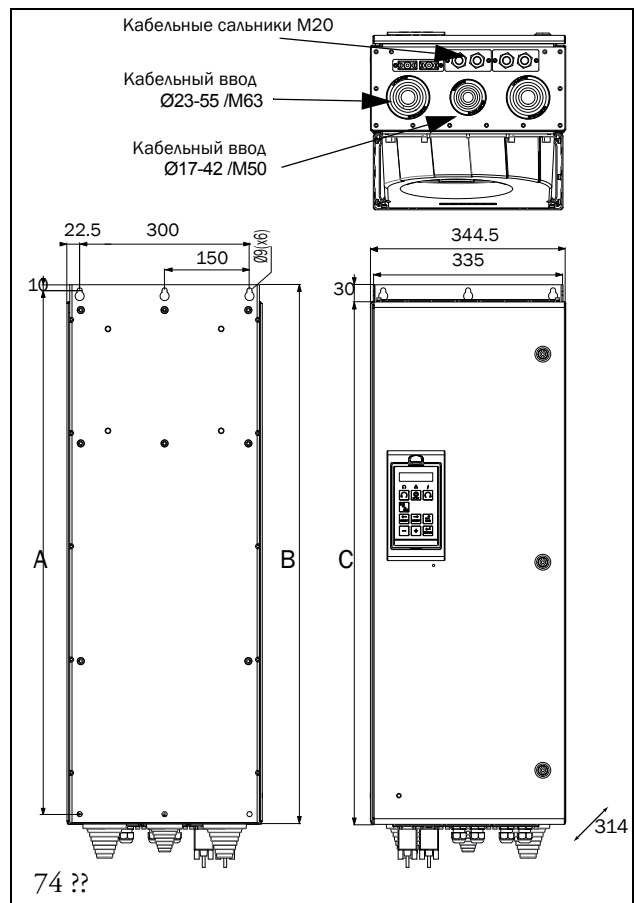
Устройство Emotron FDU моделей 48-210 - 250 (типоразмер корпуса F) Устройство Emotron FDU моделей 69-90 – 200 (типоразмер корпуса F69) с кабельным интерфейсом для подключения электрической сети, электродвигателя, опции DC+/DC-, тормозного резистора и связи
